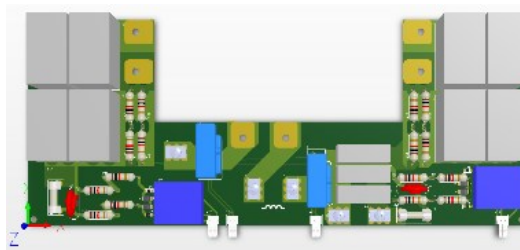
Placa de Circuito Impresso para o barramento c.c. do lado primário.
